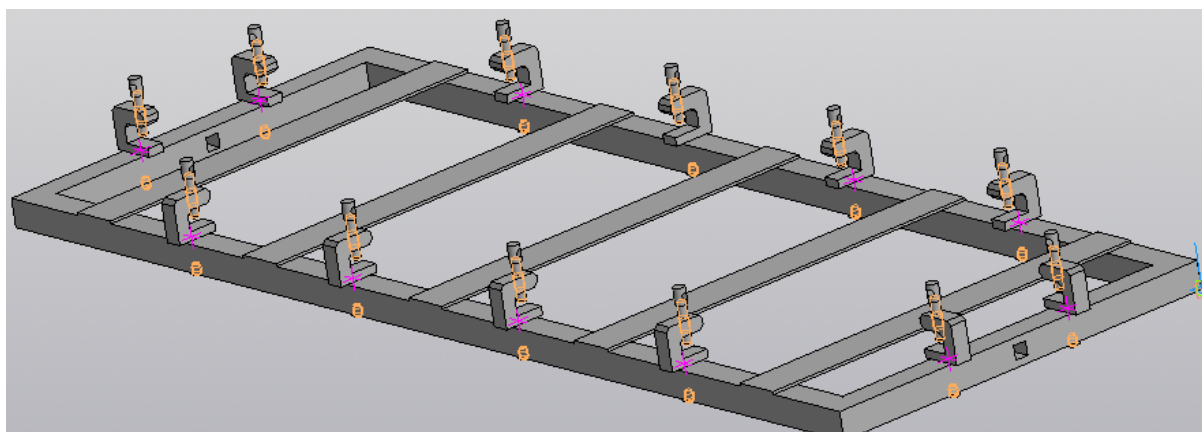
Внешний вид сборочно-сварочное приспособление ФЮРА.000001.167.00.000.СБ
